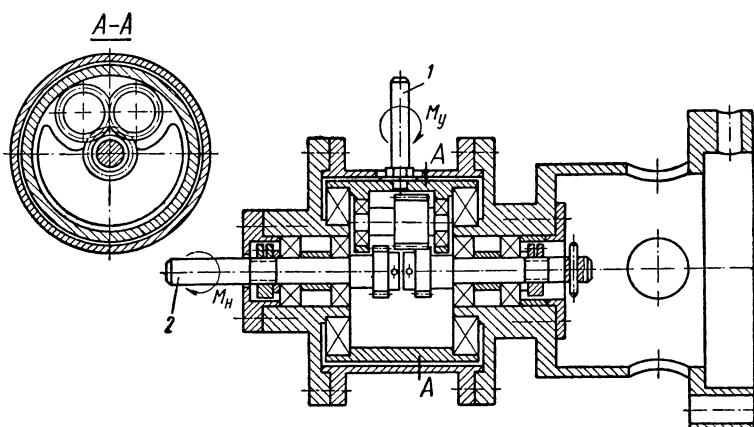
Динамометр с цилиндрическими зубчатыми колесами
